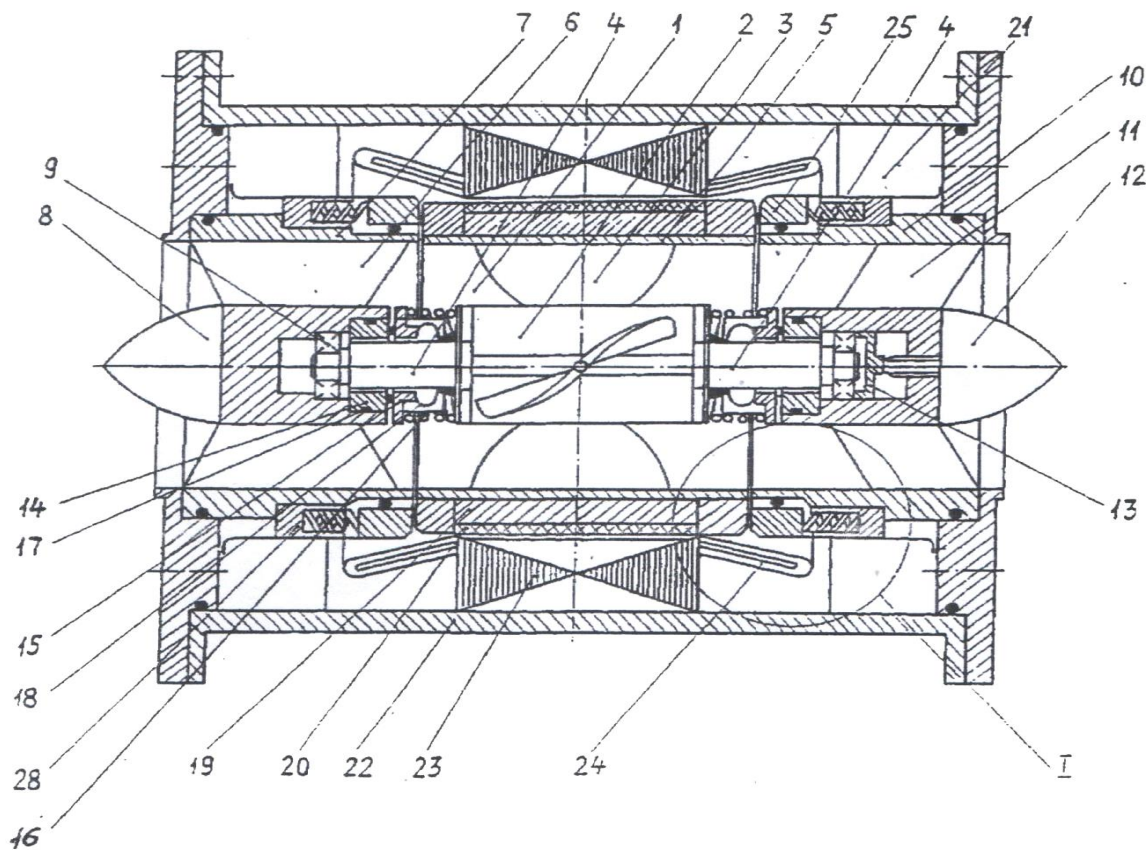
Прямоточний гідроагрегат: 1 – камера турбіни; 2 – маточина; 3 – лопаті; 4 – опорні цапфи; 5 – обід робочого колеса; 6 – направляючі лопаті; 7, 10 – зовнішня обичайка; 8, 12 – обтічник; 9, 13 – підшипниковий вузол; 11 – опорні колони; 14 і 15 – нерухоме і пружно встановлене ущільнювальне кільце; 16 – пружний елемент; 17, 18 – вторинне ущільнення; 19 – ротор; 20 – індуктор; 21 – порожнина статора генератора; 22 – корпус; 23 – сердечник; 24 – обмотка статора; 25 – механічне торцеве ущільнення; 28 – контактні пружні елементи
